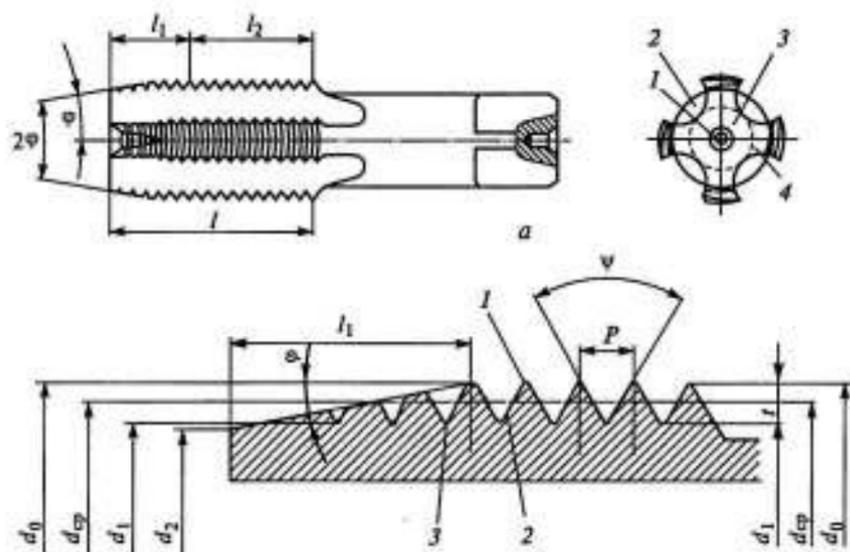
Конструктивные элементы и профиль резьбы метчика:
